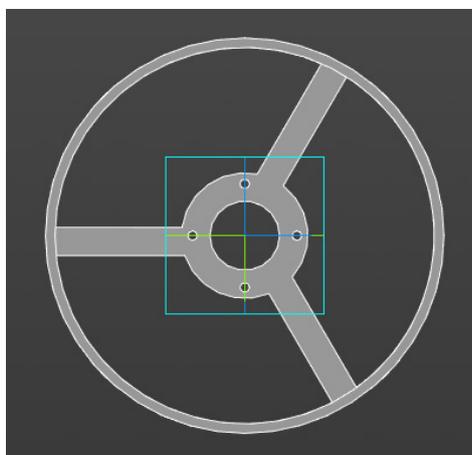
3D-модель хвостовой части ракеты, вид сверху
